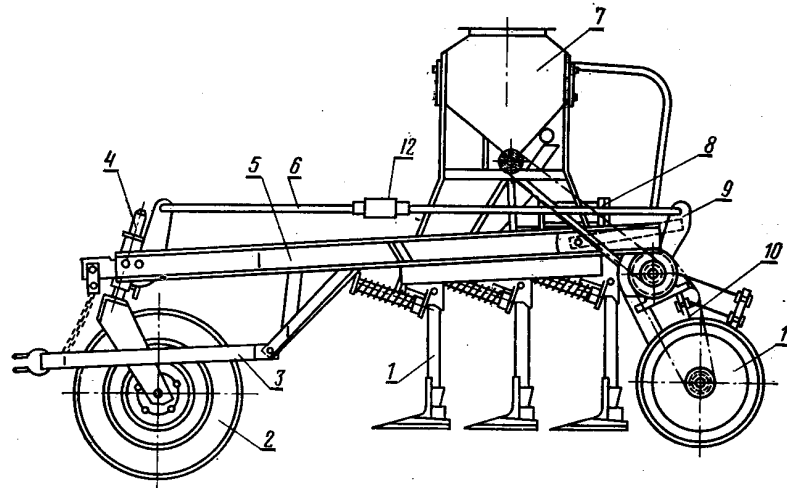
Схема сівалки СЗС-2,1: 1 – лапа-сошник; 2 – опорне колесо; 3 – причеп; 4 – вісь вилки опорного колеса; 5 – рама; 6 – тяга; 7 – насіннєвий ящик; 8 – гідроциліндр; 9 – фіксуєча планка; 10 – кронштейн котків; 11 – прикочуючі котки; 12 – стяжна гайка.
